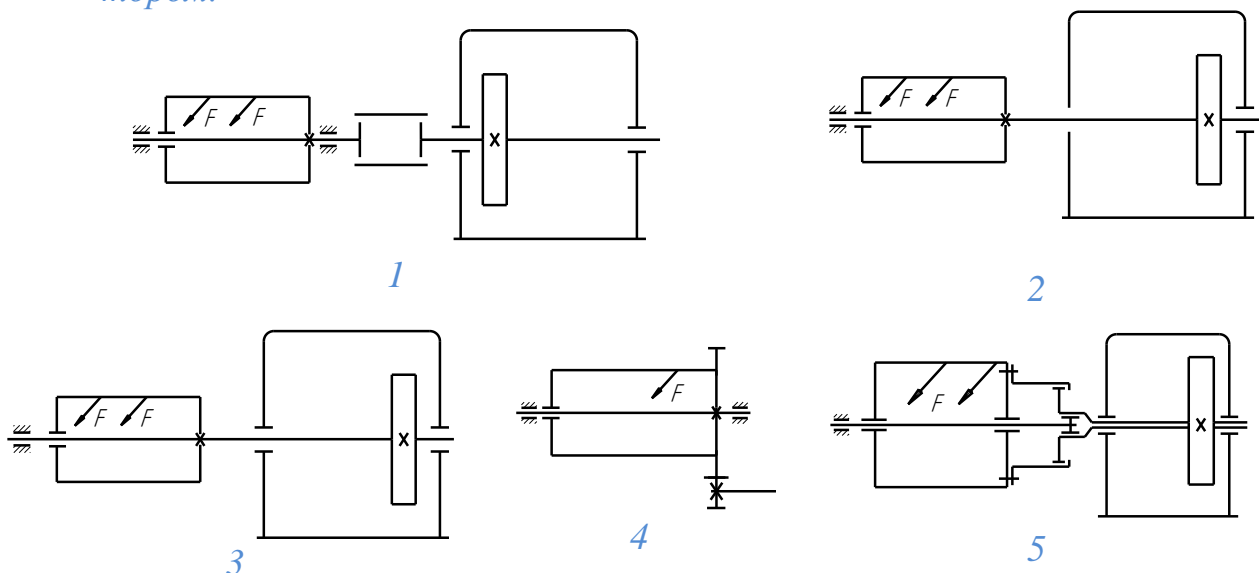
Схемы соединения барабана с редуктором
